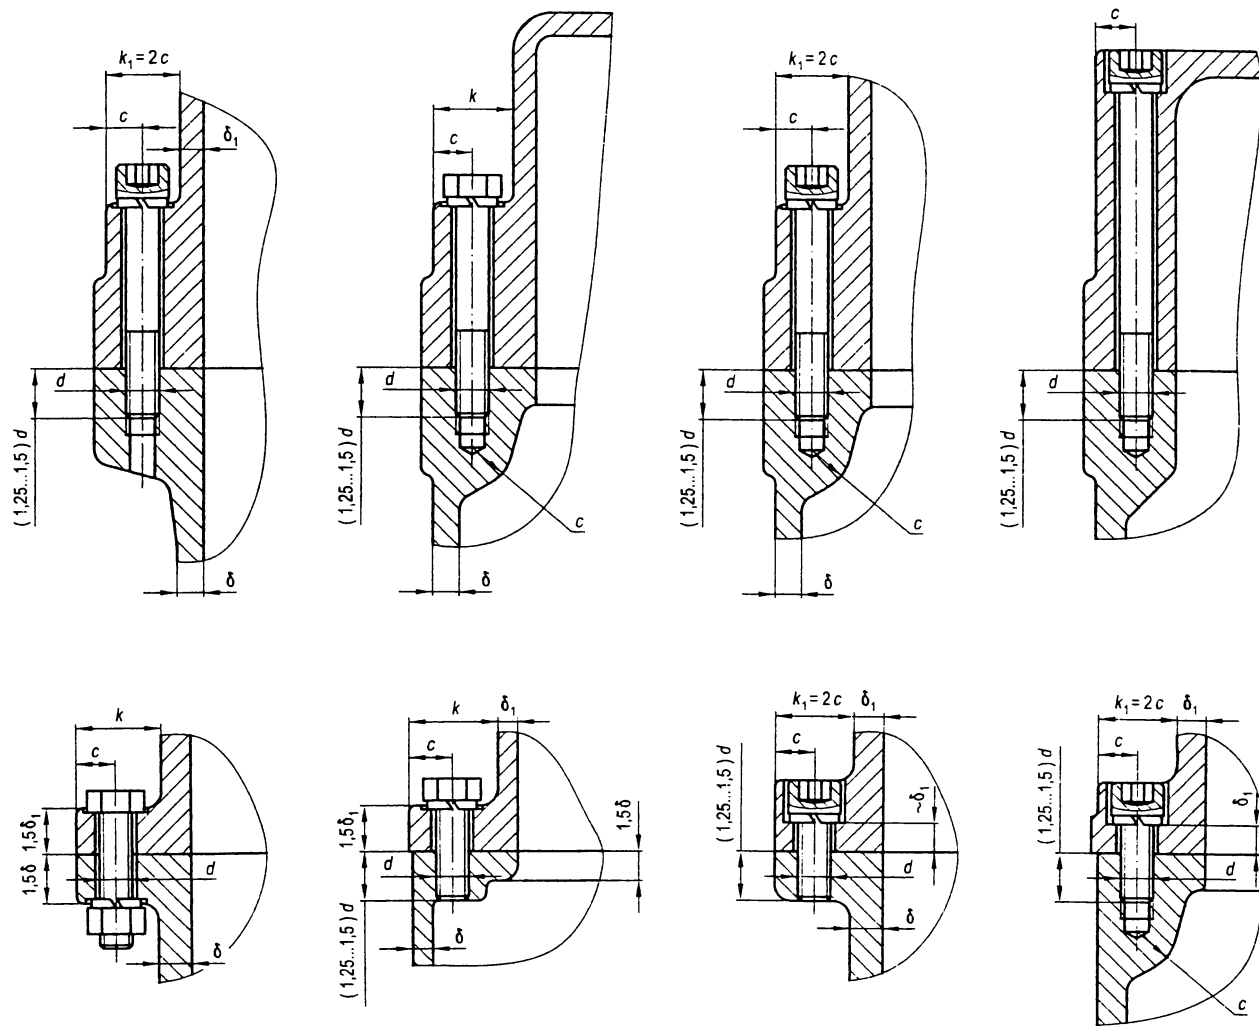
Приливы под болты и винты на боковых сторонах корпуса (размеры см. в табл. 11.2.1) [1]
